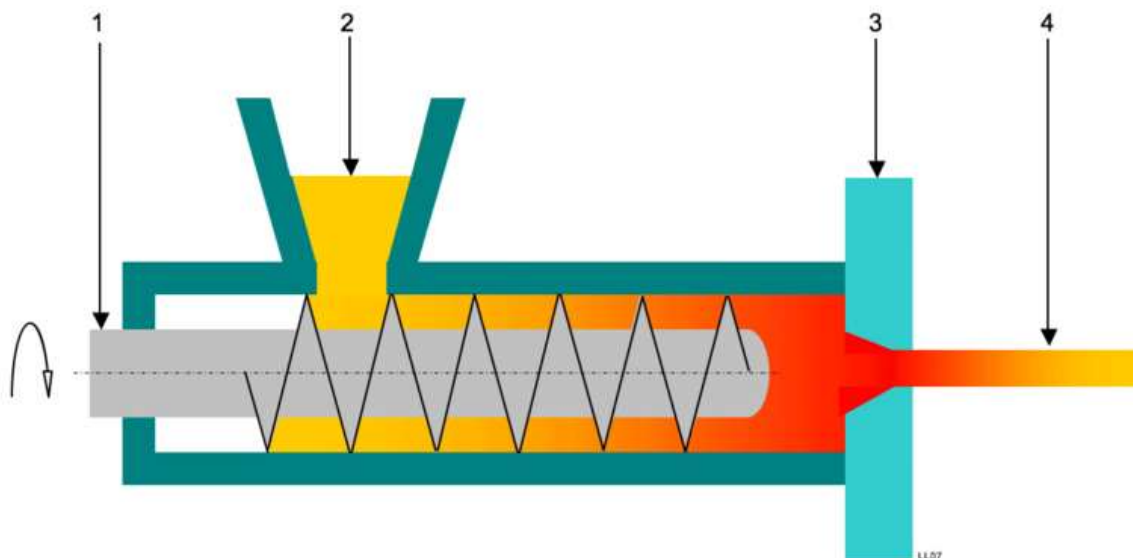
schéma du processus d'extrusion. 1) une vis pousse le polymère en fusion dans la machine. 2) entrée du PEEK en fusion. 3) moulage du PEEK. 4) produit fini. (<http://www.packaging-gateway.com>, 2014)
